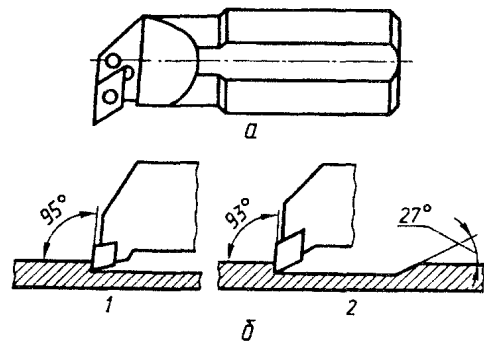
Розточувальний різець з механічним кріпленням ромбічної непереточуваної твердосплавної пластинки: а - загальний вигляд; б - типові схеми розточування: 1 - з підрізуванням уступу; 2 - з врізуванням у широку канавку під кутом
